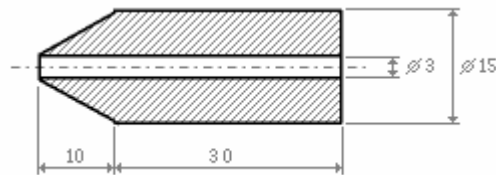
corte longitudinal do grave usado. As dimensões estão em milímetros.
